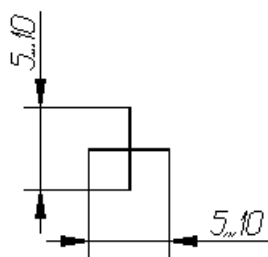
Условное изображение одиночной сварной точки
